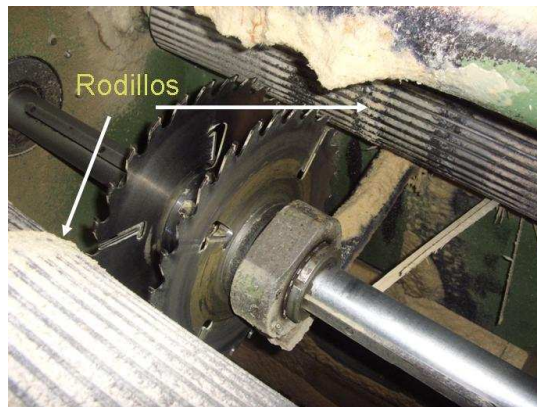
Rodillos de presión en el interior de la máquina CB 10
